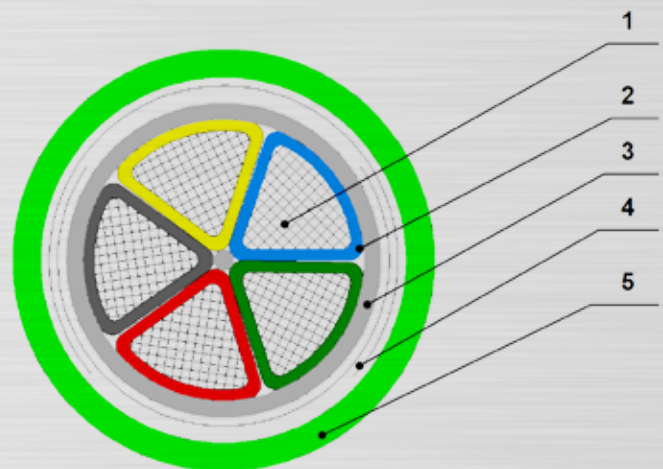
Конструкция кабеля марки ПвБПнг(А)-НФ на напряжение 1 кВ: 1 – токопроводящая жила; 2 – изоляция; 3 – внутренняя оболочка; 4 – броня; 5 – наружная оболочка
